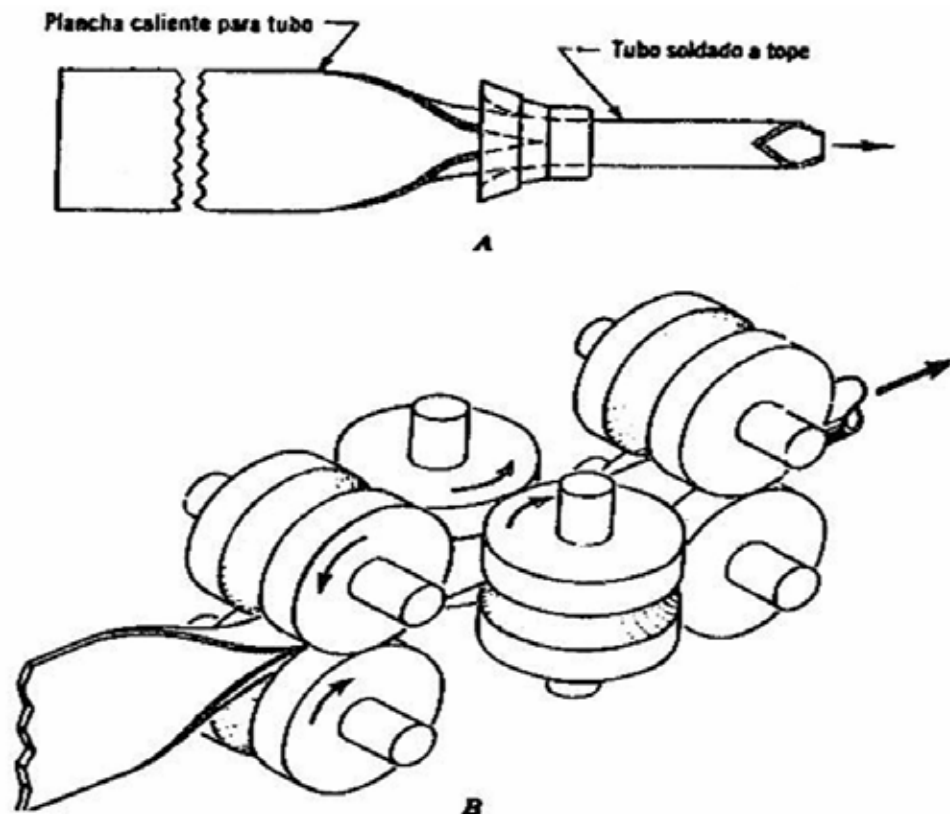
Producción de Tubo Soldado a Tope
